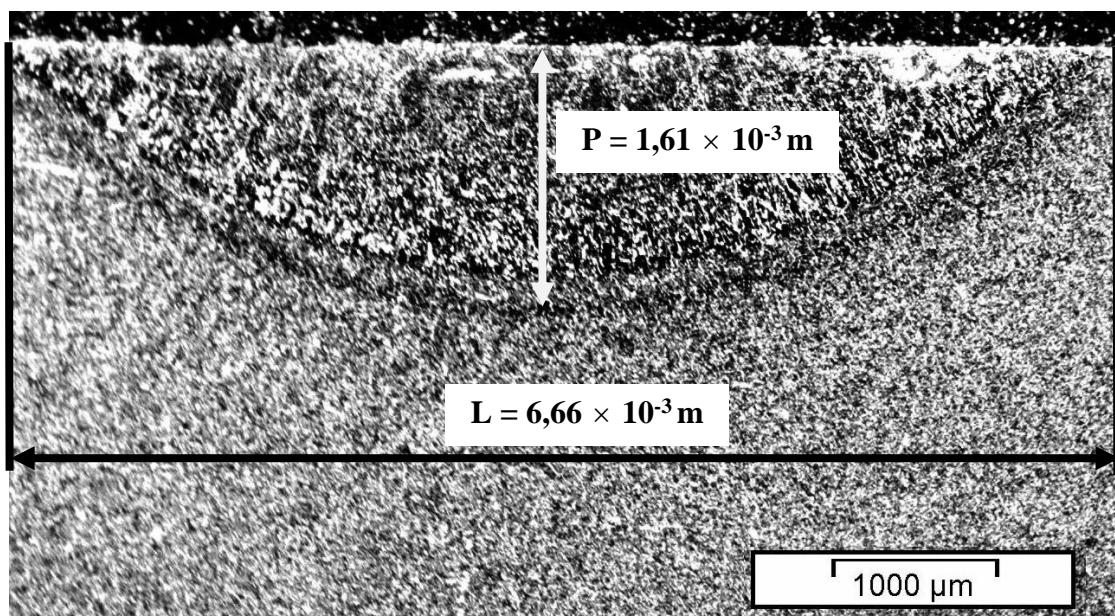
Largura e penetração do cordão de solda para condição de $t+ = 7\text{ms}$.
